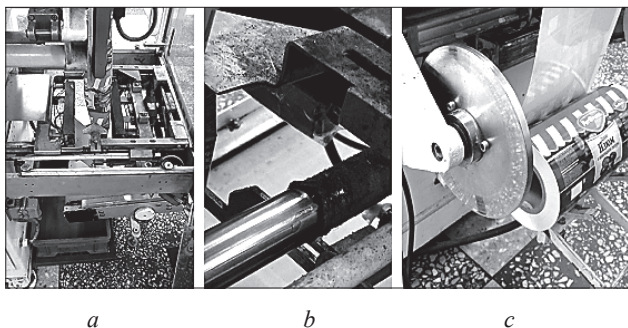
Автоматическая упаковочная машина: а – исполнительные механизмы; б – износ направляющей; с – износ приводного диска
